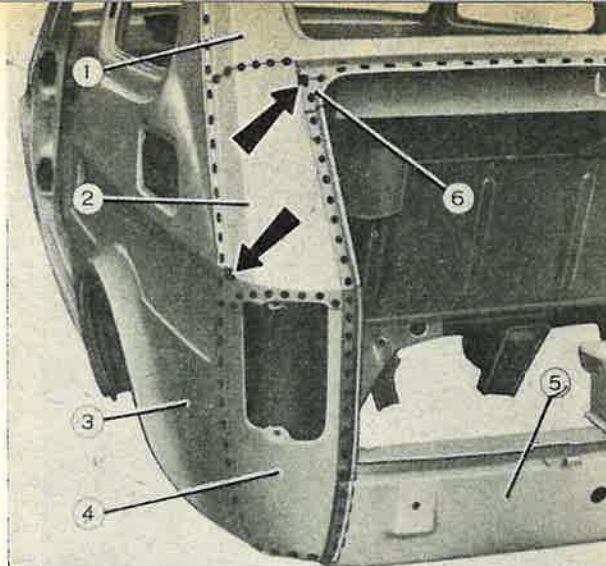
Liaisons par points de soudure, du côté de caisse aux pièces arrière.
